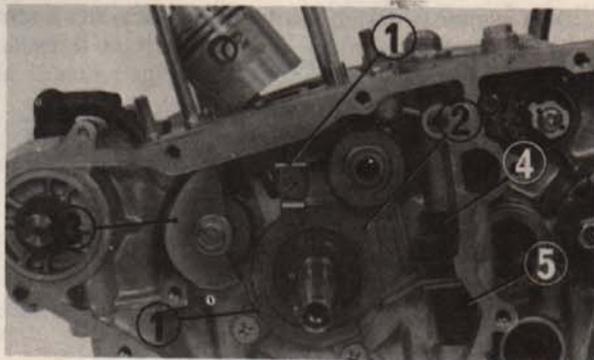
(1) Plaquette d'arrêt (4) Tige de poussée
